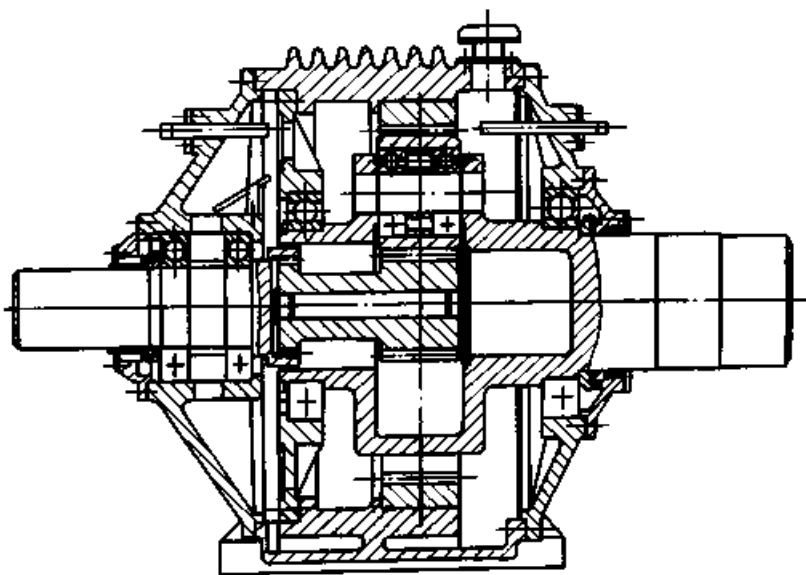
ZKD、ZZD 行星齿轮减速器结构
